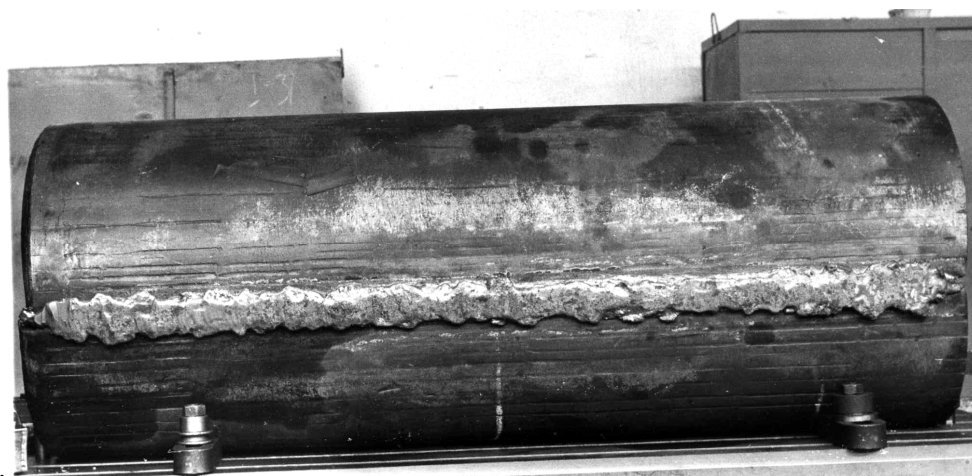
Сварная заготовка медной гильзы кристаллизатора
